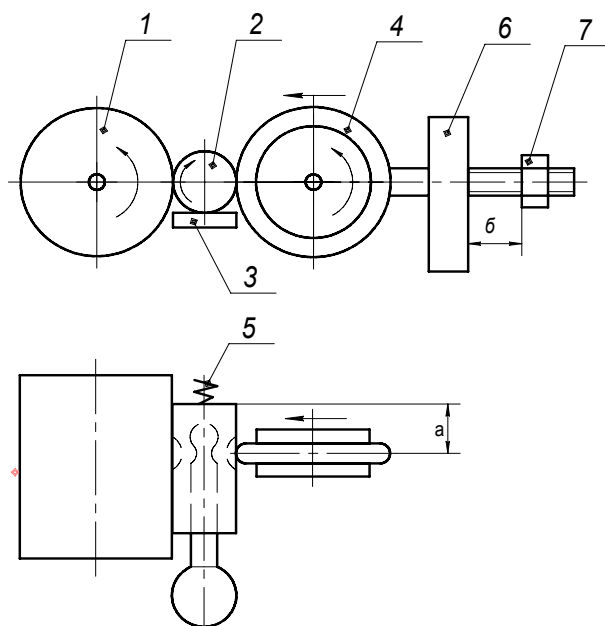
Схема пристрою АП-999 різьбонакатного верстата ГД-8 для заковування поршня із шатуном:
